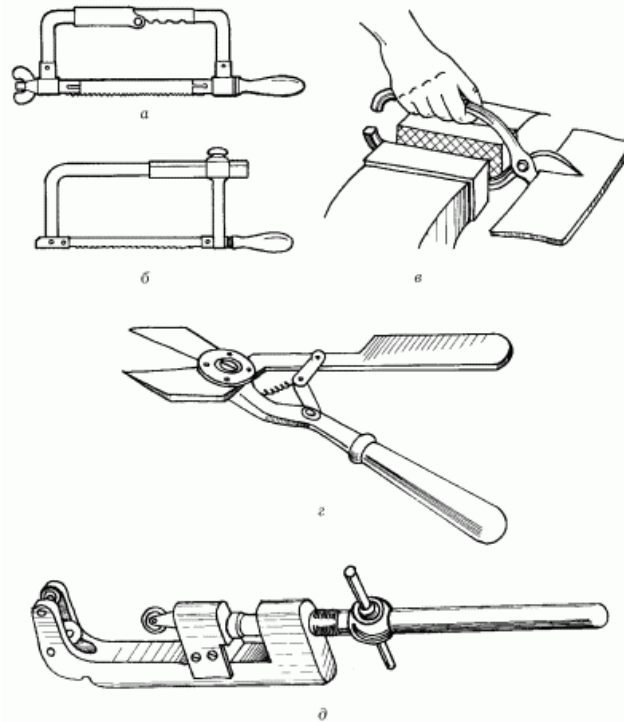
Инструменты для резки металла: а – ножовка; б – лобзик; в – ручные ножницы; г – силовые ножницы; д – труборез.
